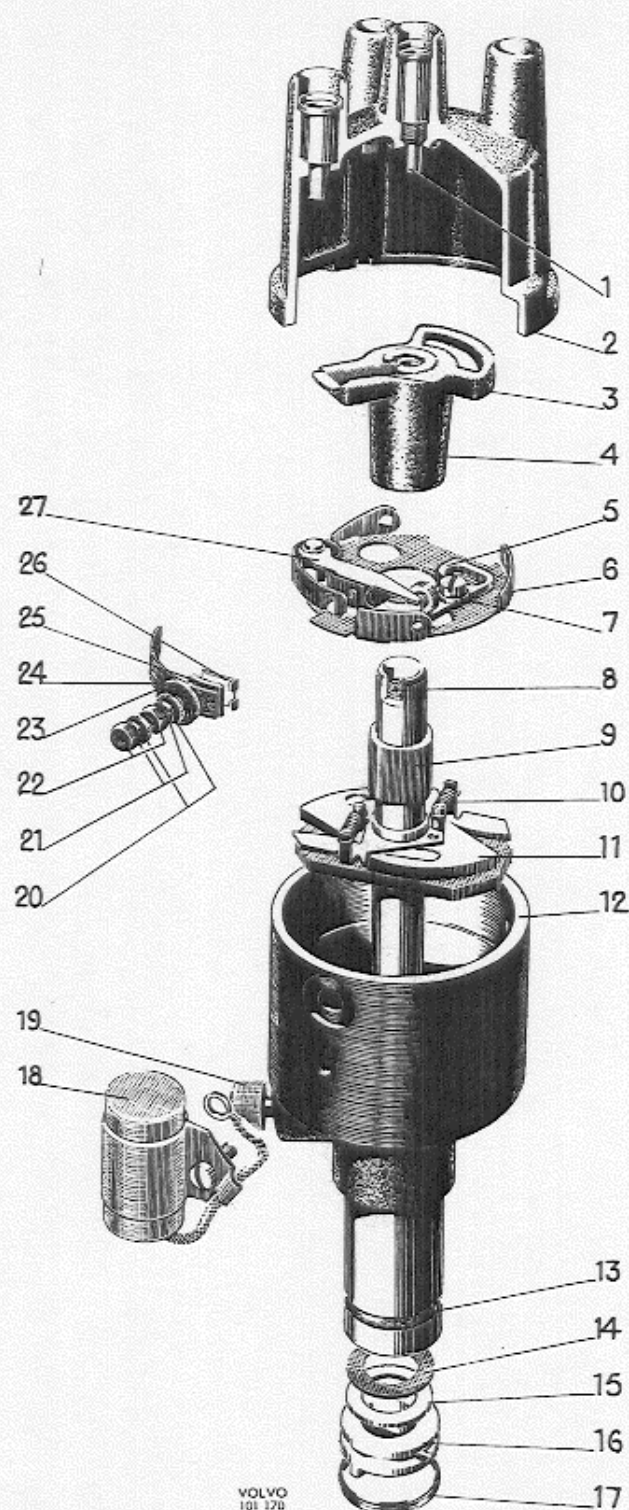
Zündverteiler, Motor B 18 D, spätere Ausführung
